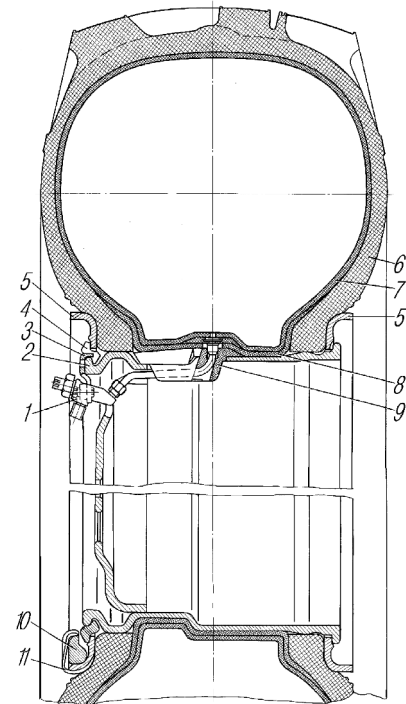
Колесо с шиной в сборе: 1- кран колесный; 2- основание обода с диском; 3- ограничитель замочного кольца; 4- кольцо замочное; 5- кольцо бортовое; 6- крышка; 7- камера; 8- лента ободная; 9- уплотнитель вентильного паза; 10- груз балансировочный; 11- пружина балансировочного груза
